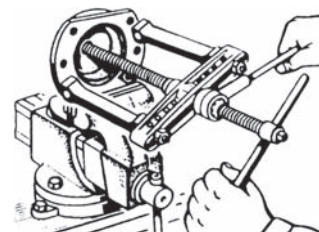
Выпрессовка внешней обоймы подшипника № 7610K1 из стакана вторичного вала.
